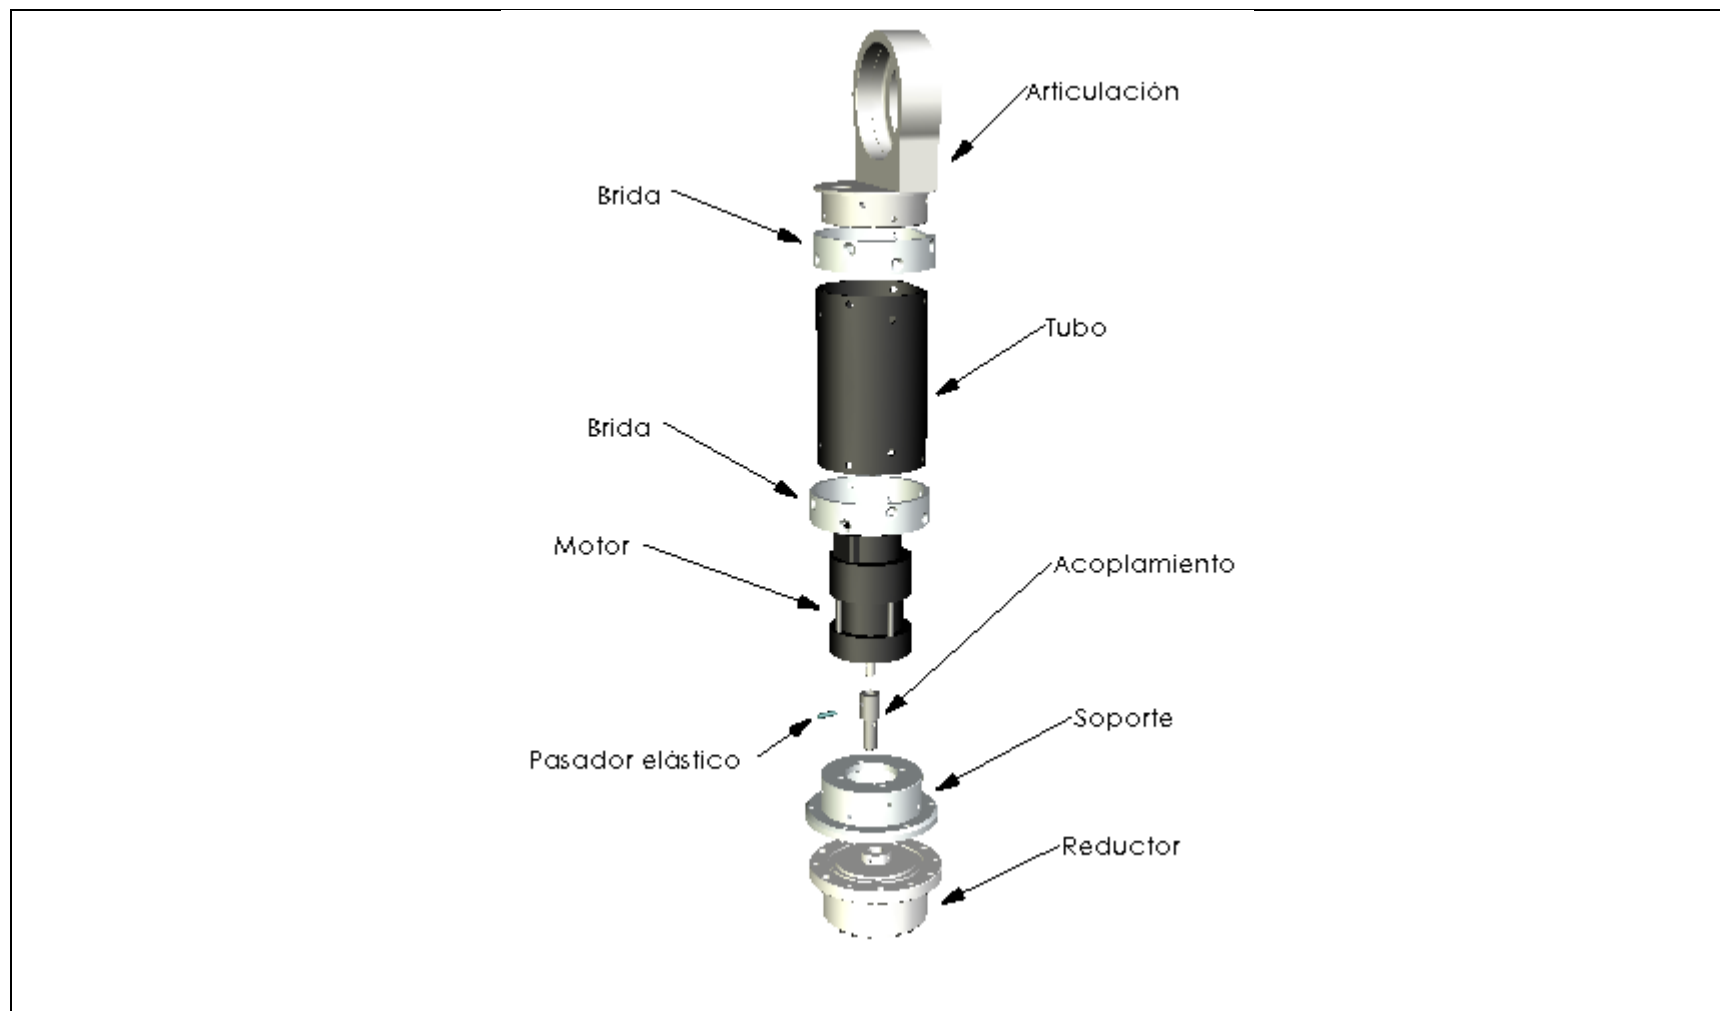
Vista explosionada del sub-ensamblaje 4.
